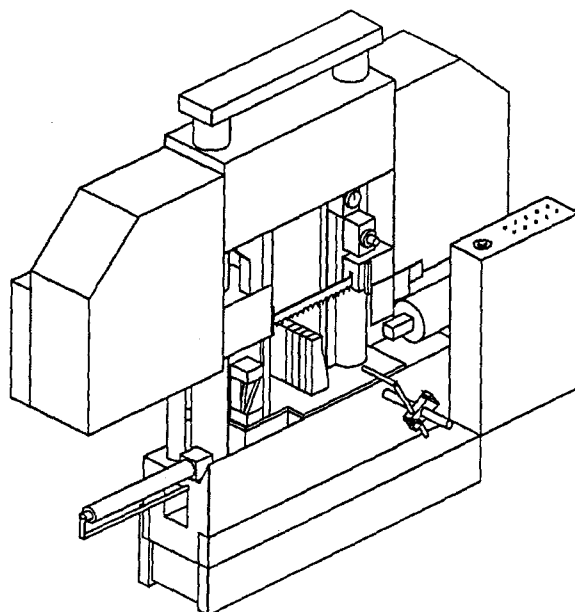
Горизонтальний стрічковопиляльний верстат з колоною
